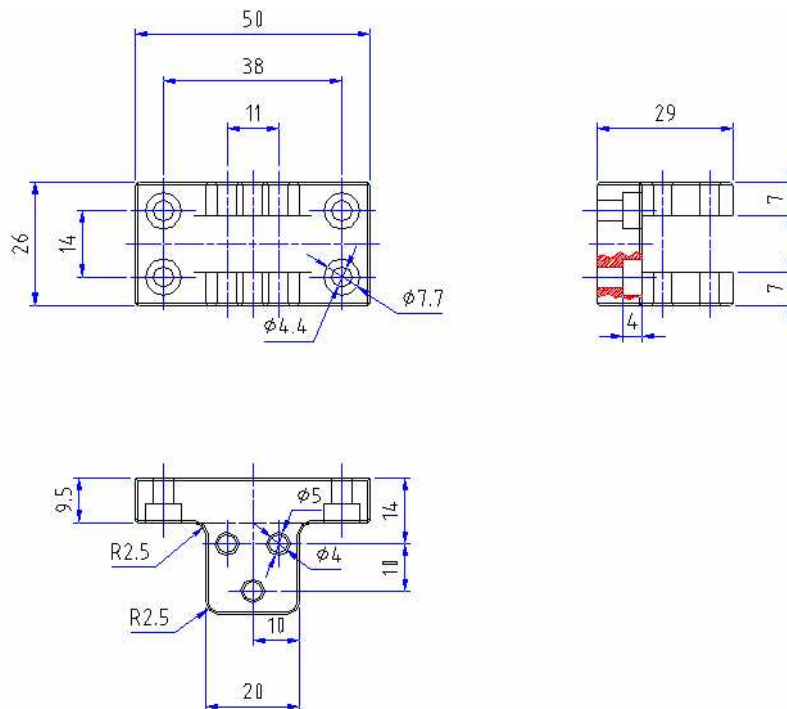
Geometria e dimensões dos suportes de fixação das células de carga (mm).
